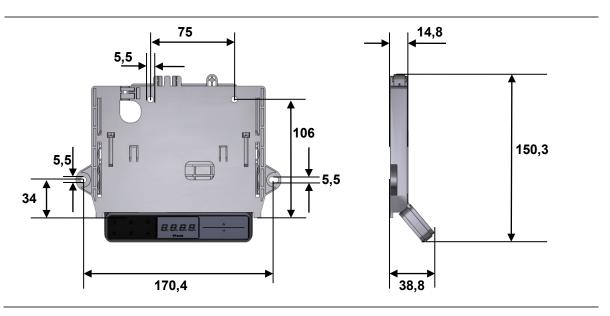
Bedienelement TOUCHdown, Montagemaße (Angaben in mm)
